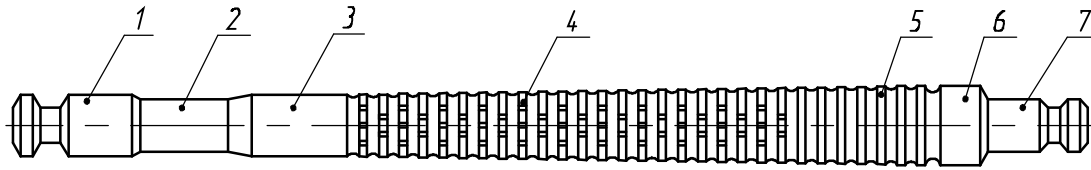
Конструктивные элементы протяжки с круглыми зубьями.
